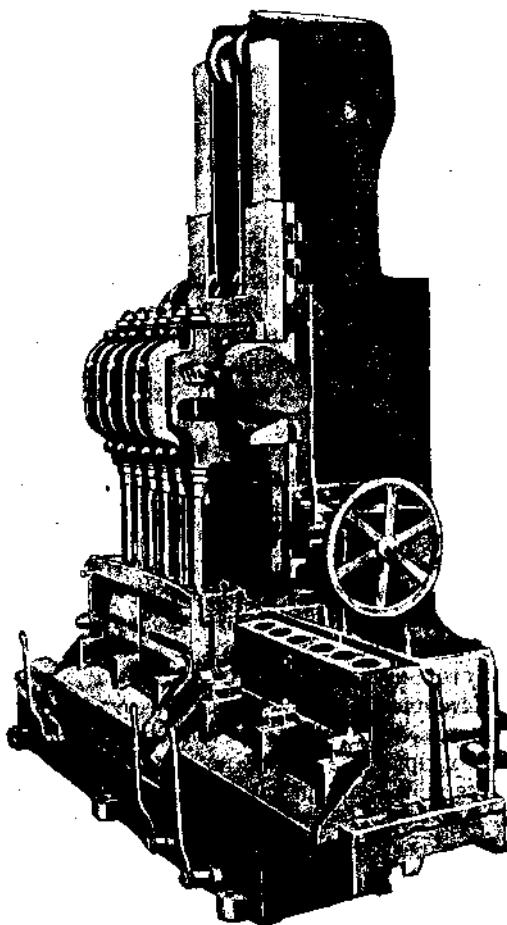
Станок для расточки автомобильных блоков фирмы Holroyd.
